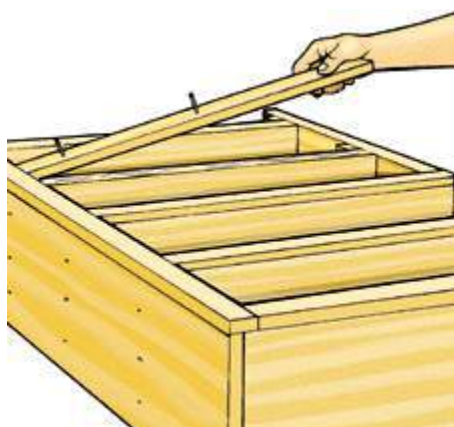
Fije las tiras de 1 x 2 a la caja comenzando con un miembro vertical. Luego, agrega las piezas horizontales y las otras verticales.
